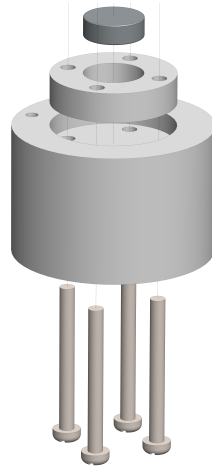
Vista explodida da parte inferior do gerador eletromagnético adaptativo.
